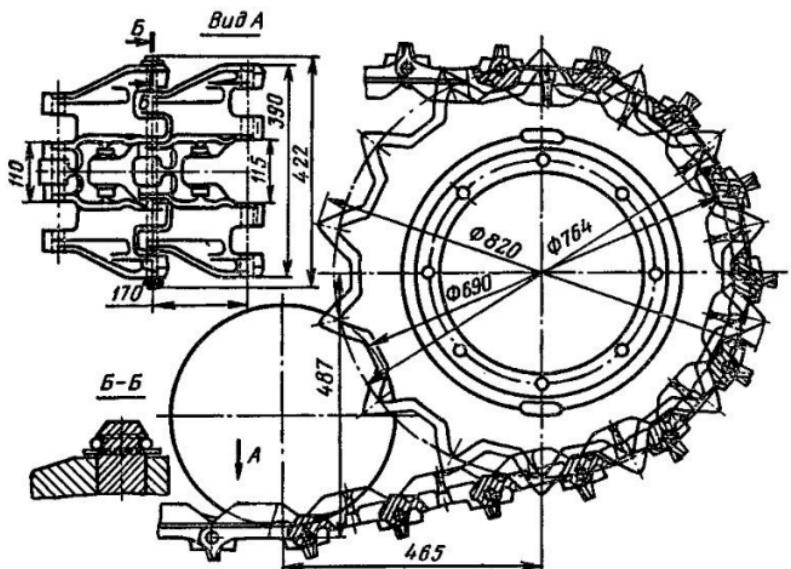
Гусеничная цепь из семипроушиных цельнолитых звеньев цевочного зацепления с металлическим открытым шарниром тракторов тягового класса 3.
